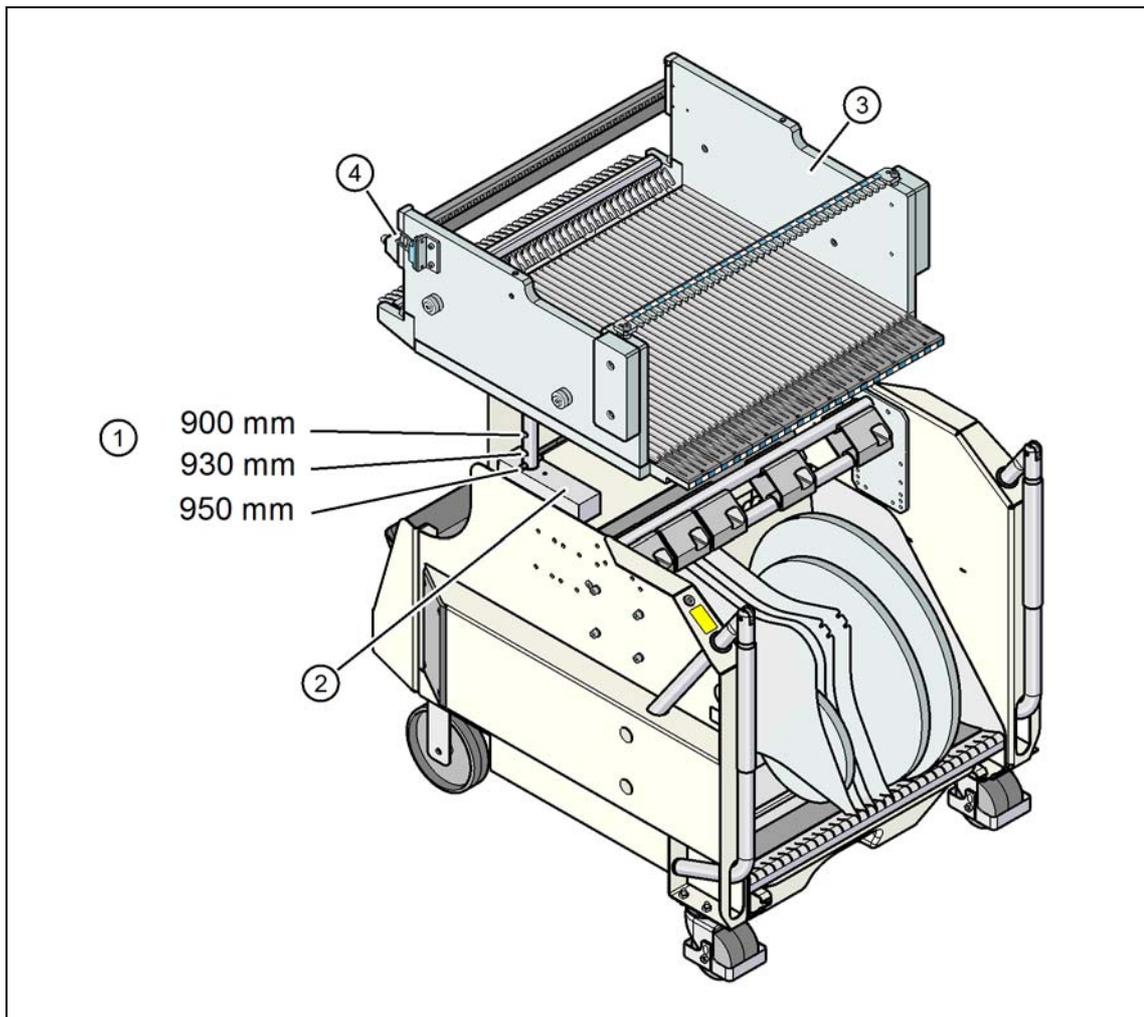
2 料车 (SIPLACE X 系列), PCB 传送导轨高度为 950 mm
